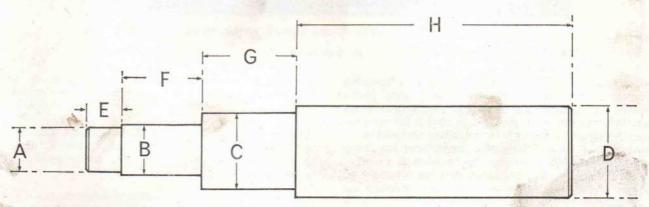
MANDRIN DE GUIDAGE DES DISQUES D'EMBRAYAGE
